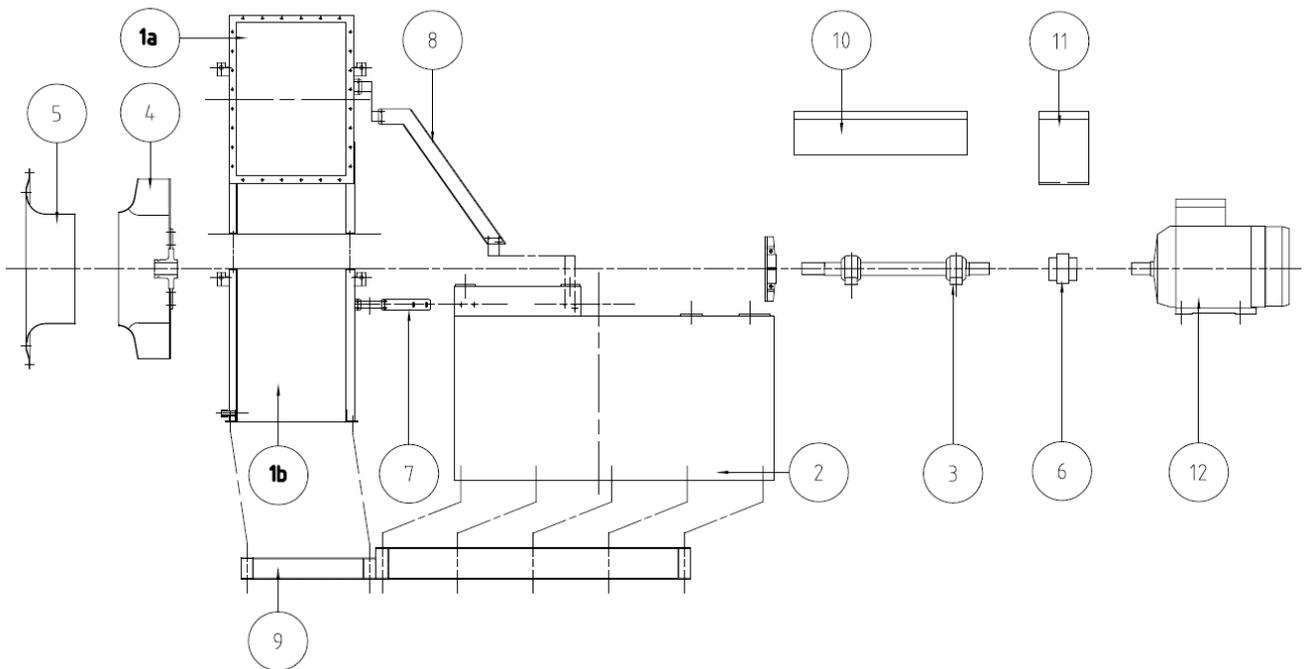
Assemblaggio di ventilatore in esecuzione 8
